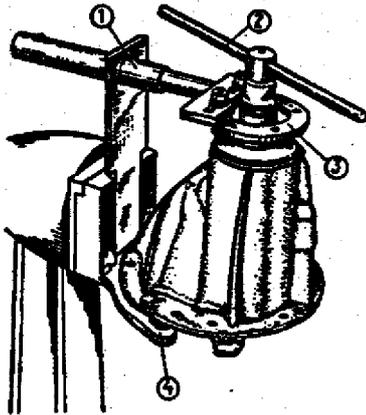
Remoção da porca do flange do pinhão: 1 - dispositivo para fixar o flange do pinhão; 2 - chave com soquete; 3 - flange do pinhão; 4 - suporte.
